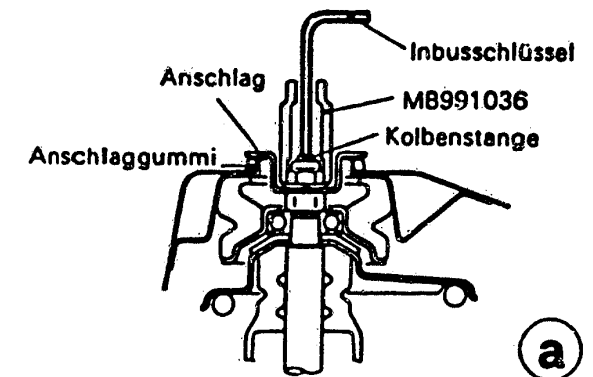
a) Die obere Befestigung des Federbeins lässt sich mit einem Spezialwerkzeug vom Motorraum her lösen.
